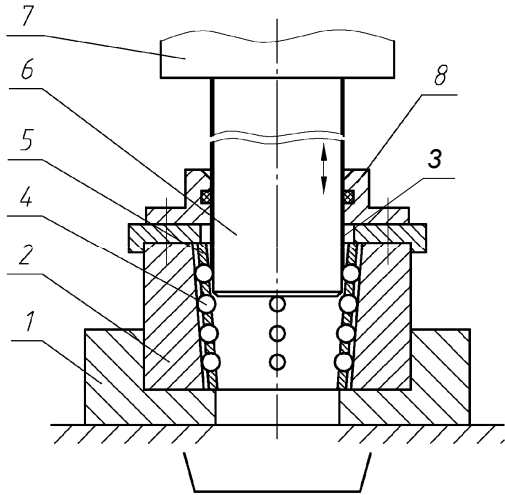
Інструмент для дорнування напівкруглих шліцьових канавок валів та направляючих: 1 – корпус; 2 – матриця; 3 – напівкругла канавка; 4 – кульки; 5 – сепаратор; 6 – оброблюваний вал; 7 – повзун; 8 – направляюча (Пат. №48236, Україна)
